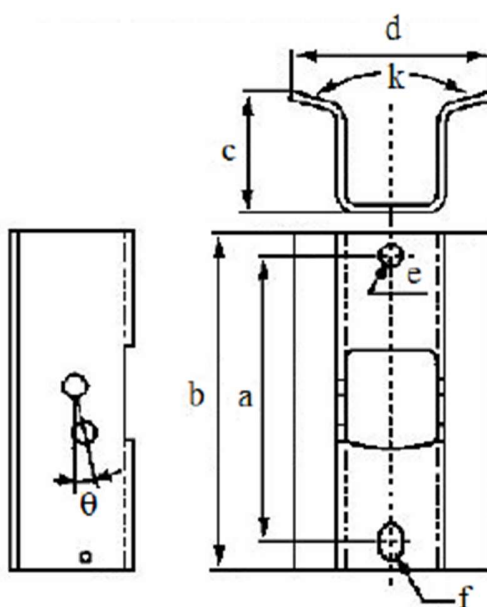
Acoplamiento tipo base flexible hacia el lado de la estructura
